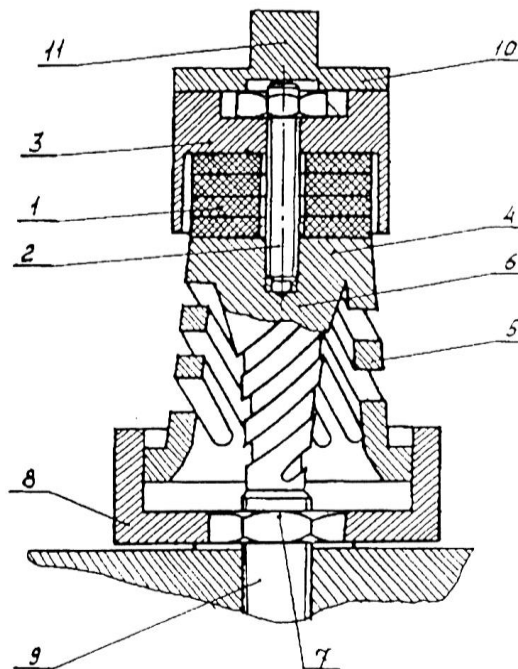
Спосіб розбирання різьбових з'єднань: 1- п'єзокерамічний перетворювач; 2- шпилька; 3- корпус; 4- частотнопонижувальний елемент разом з торсіоном 5 і коцентратором 6; 7- відгвинчувальна гайка; 8- наконечник; 9- болт; 10, 11- перехідник і квадрат.
